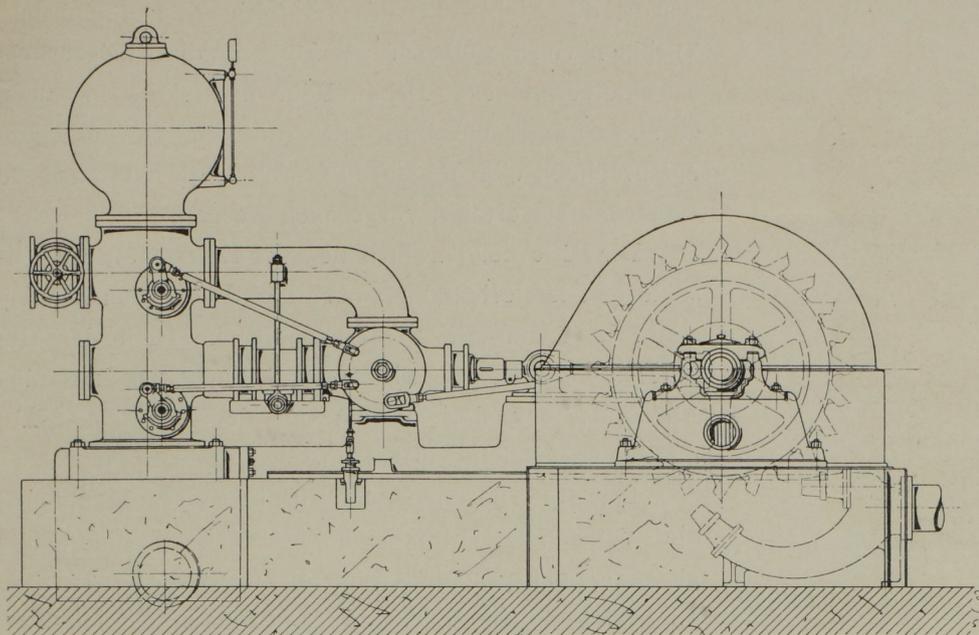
Seitenansicht der Pumpe mit Antriebsrad.
